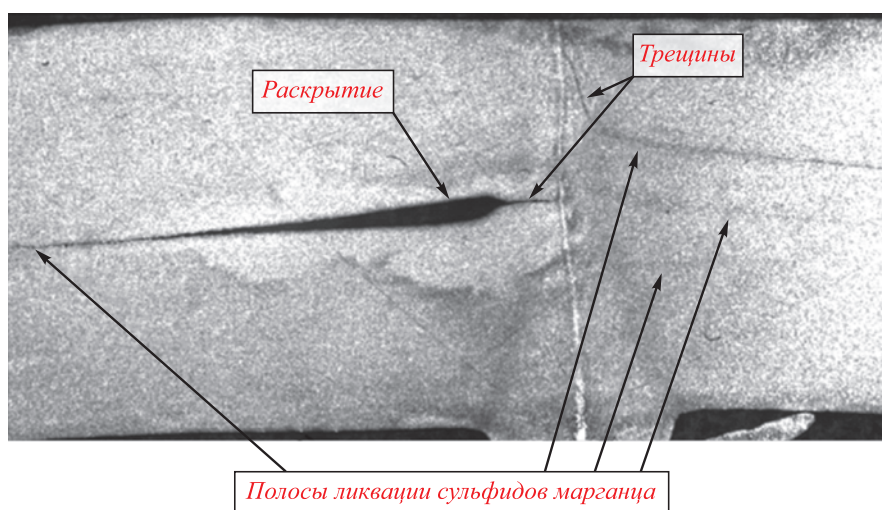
Дефекты при высокочастотной стыковой сварке труб
